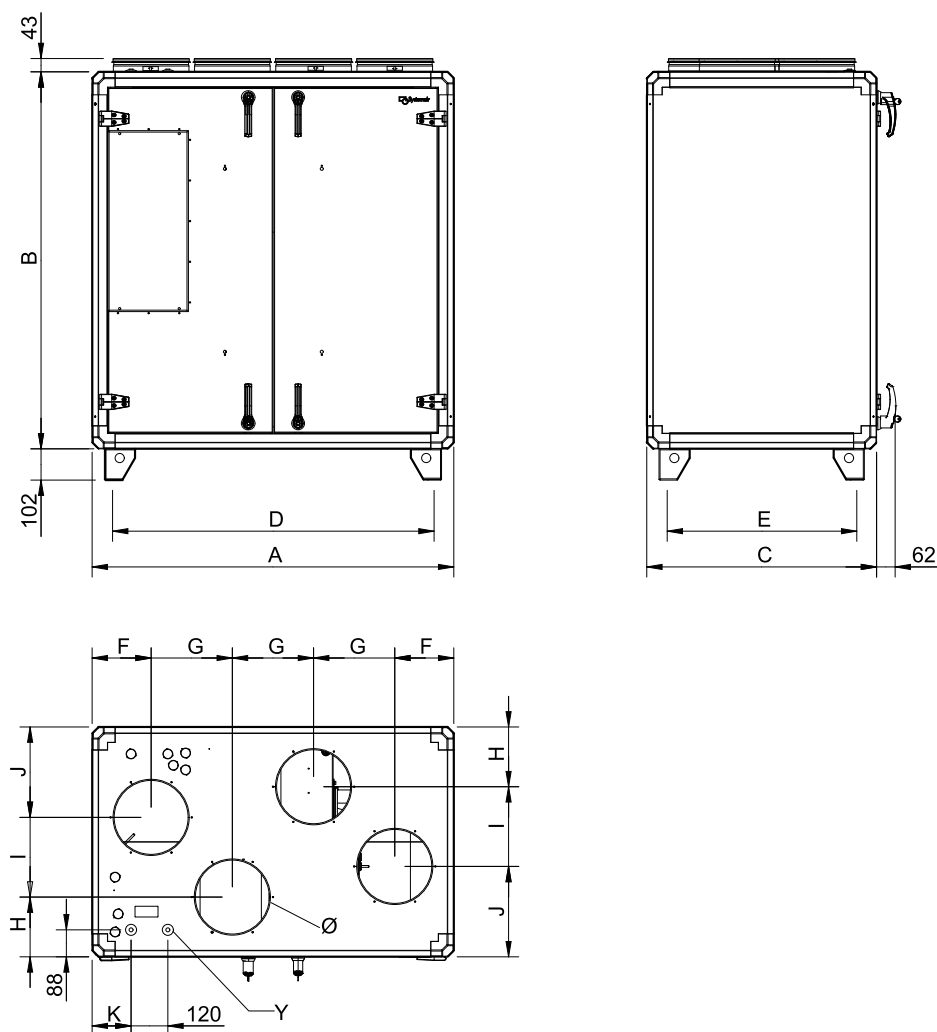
Dimensions (mm) TR03, TR04 (Version côté gauche)
